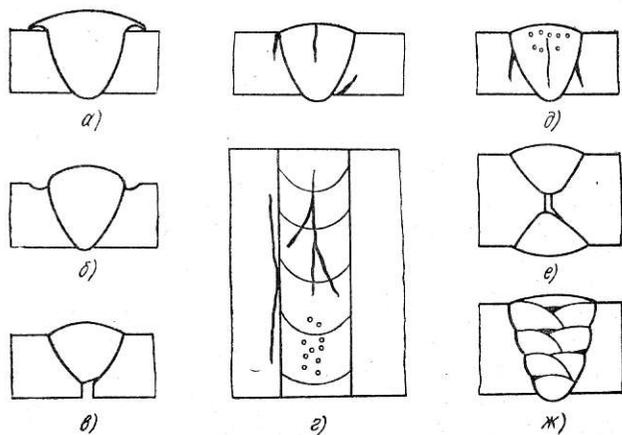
Виды дефектов в сварных соединениях
